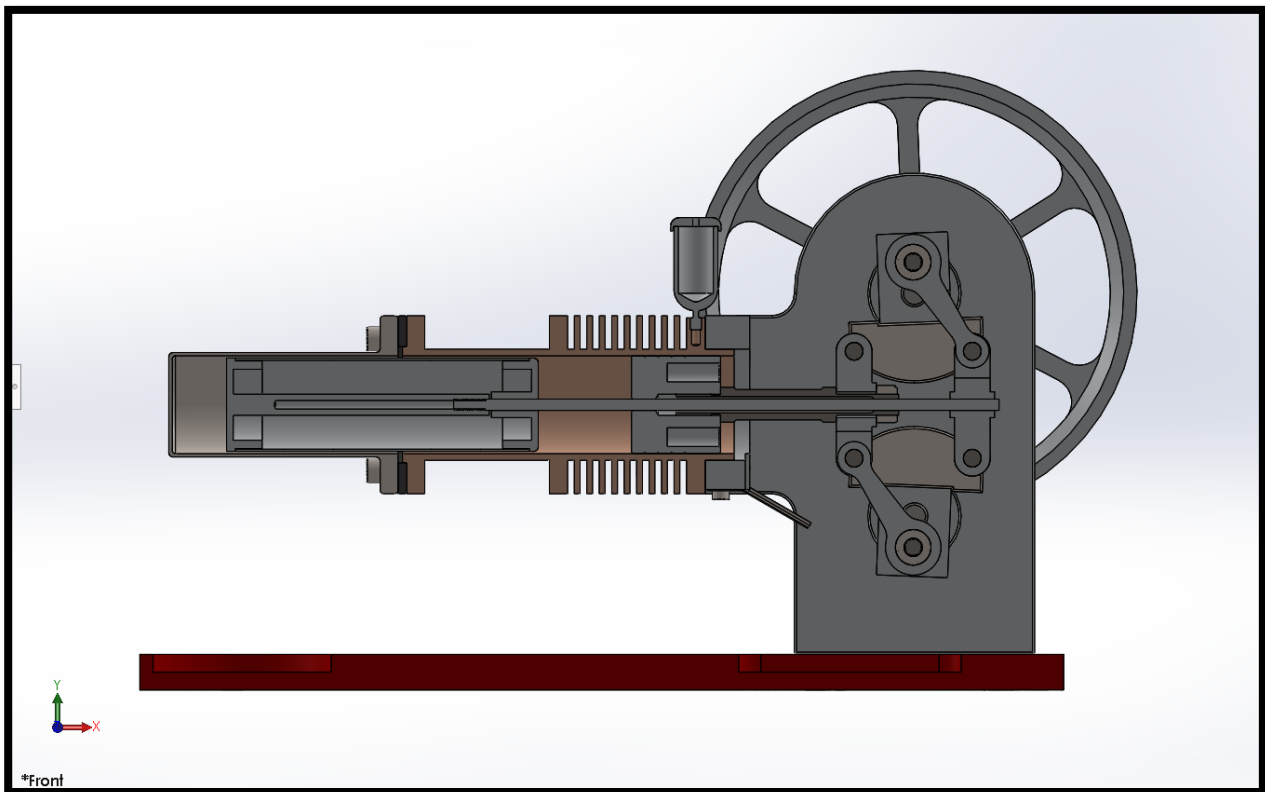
Vista de alzado del conjunto en SolidWorks.
